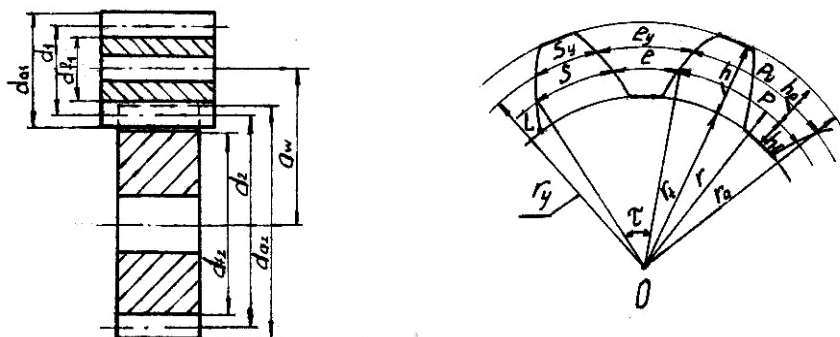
Сечение цилиндрического зубчатого колеса
